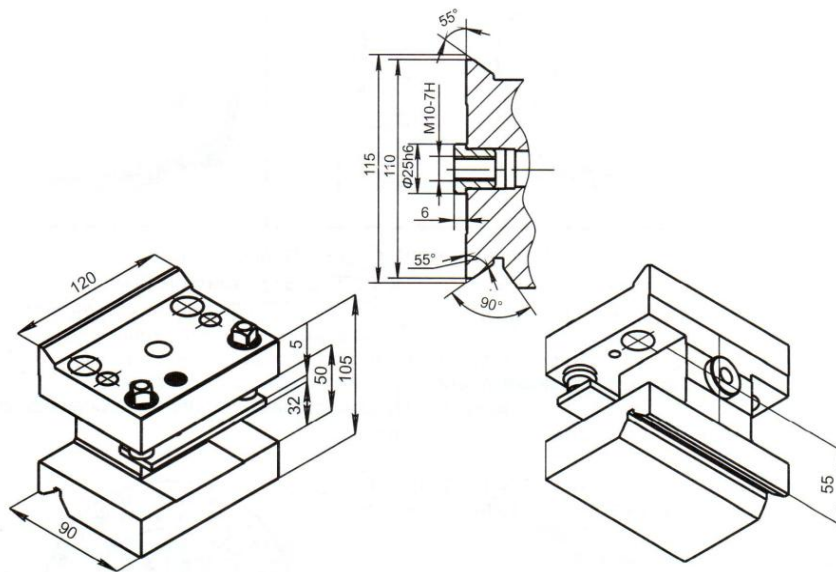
Схема резцедержателя с базирующей призмой и открытым пазом
